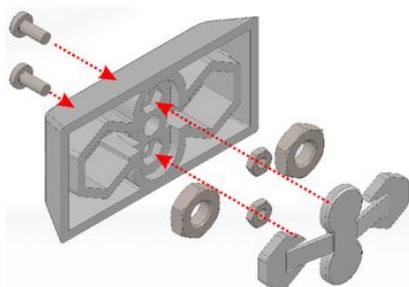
Montaje de los componentes del fijador instalado en el ITSCAM 600
